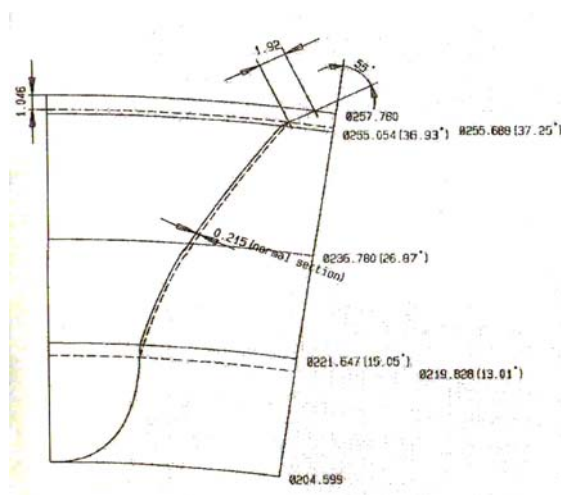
Профиль зуба под зубошлифование без шлифования впадины
